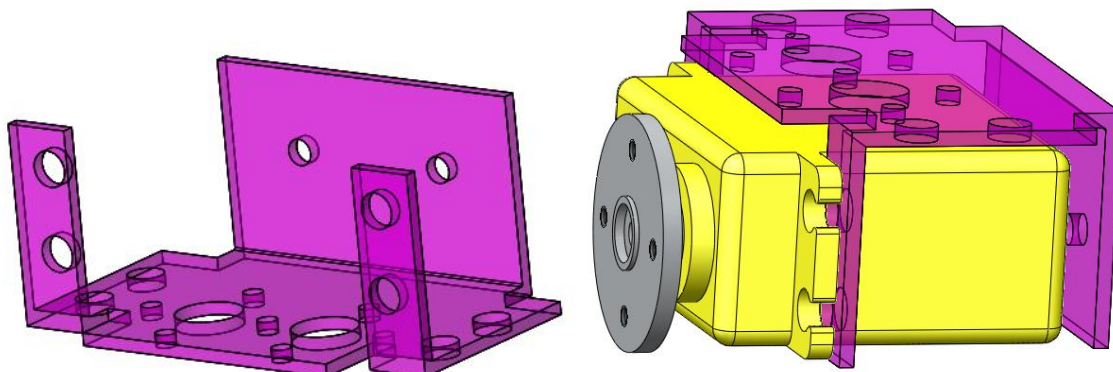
7 a) carcasa soporte b) motor montado en carcasa
